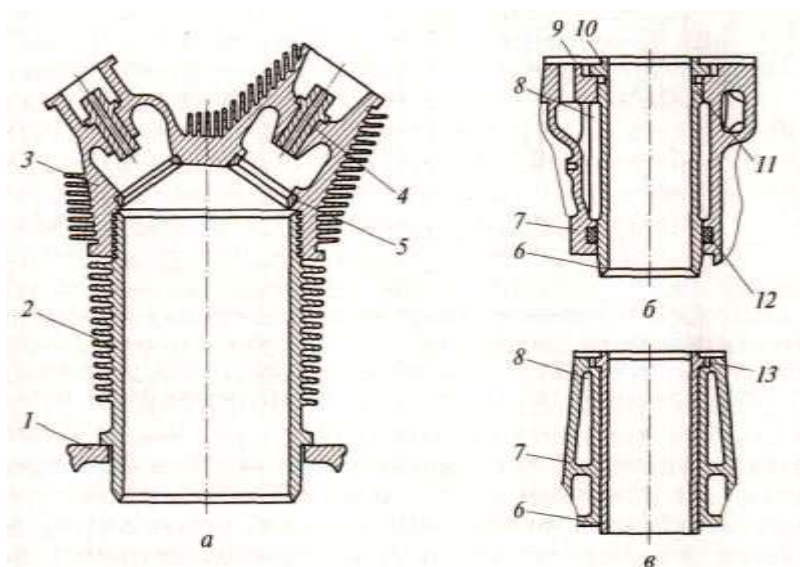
Цилиндр и гильзы цилиндров двигателя:
